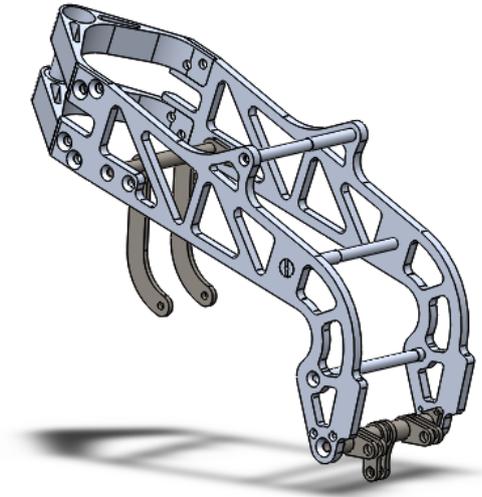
Bastidor de aluminio atornillado (gris claro) con conjunto de acero mecanizado y soldado (gris oscuro)
